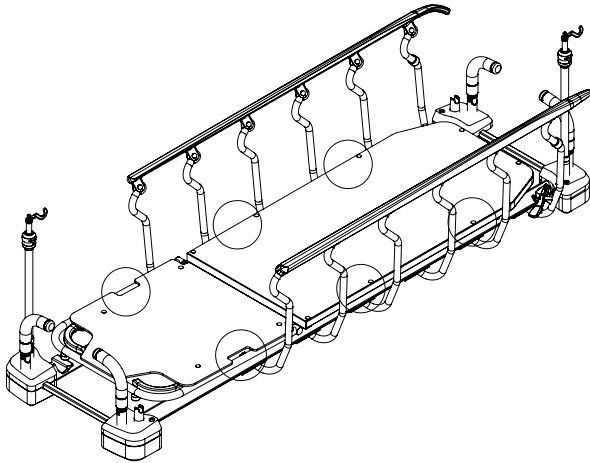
Fissaggio del supporto per il rotolo di carta
